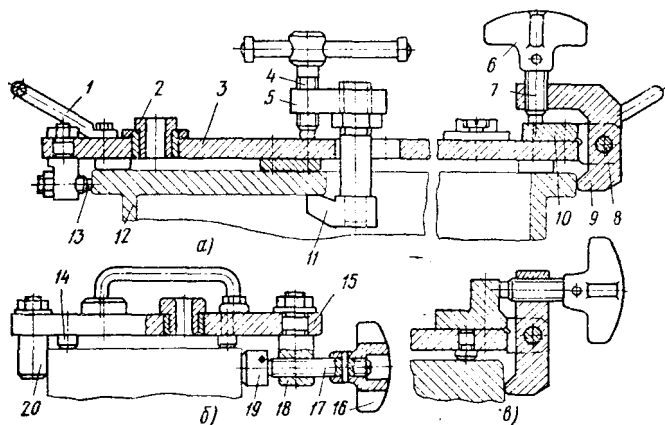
Накладные кондукторы с базированием по контуру деталей
